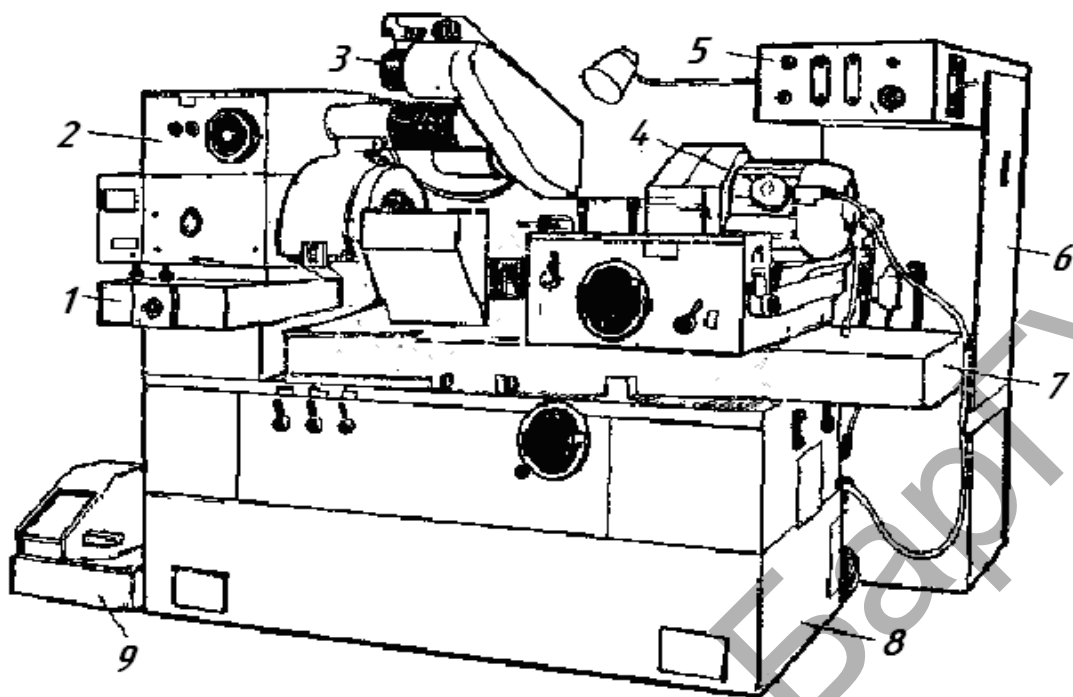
Общий вид универсального внутришлифовального станка модели 3К227В
